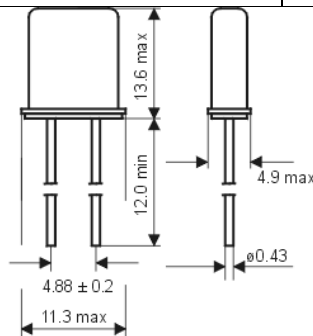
Габаритні розміри кварцового резонатора КХ-ЗНТ-8 МГц
